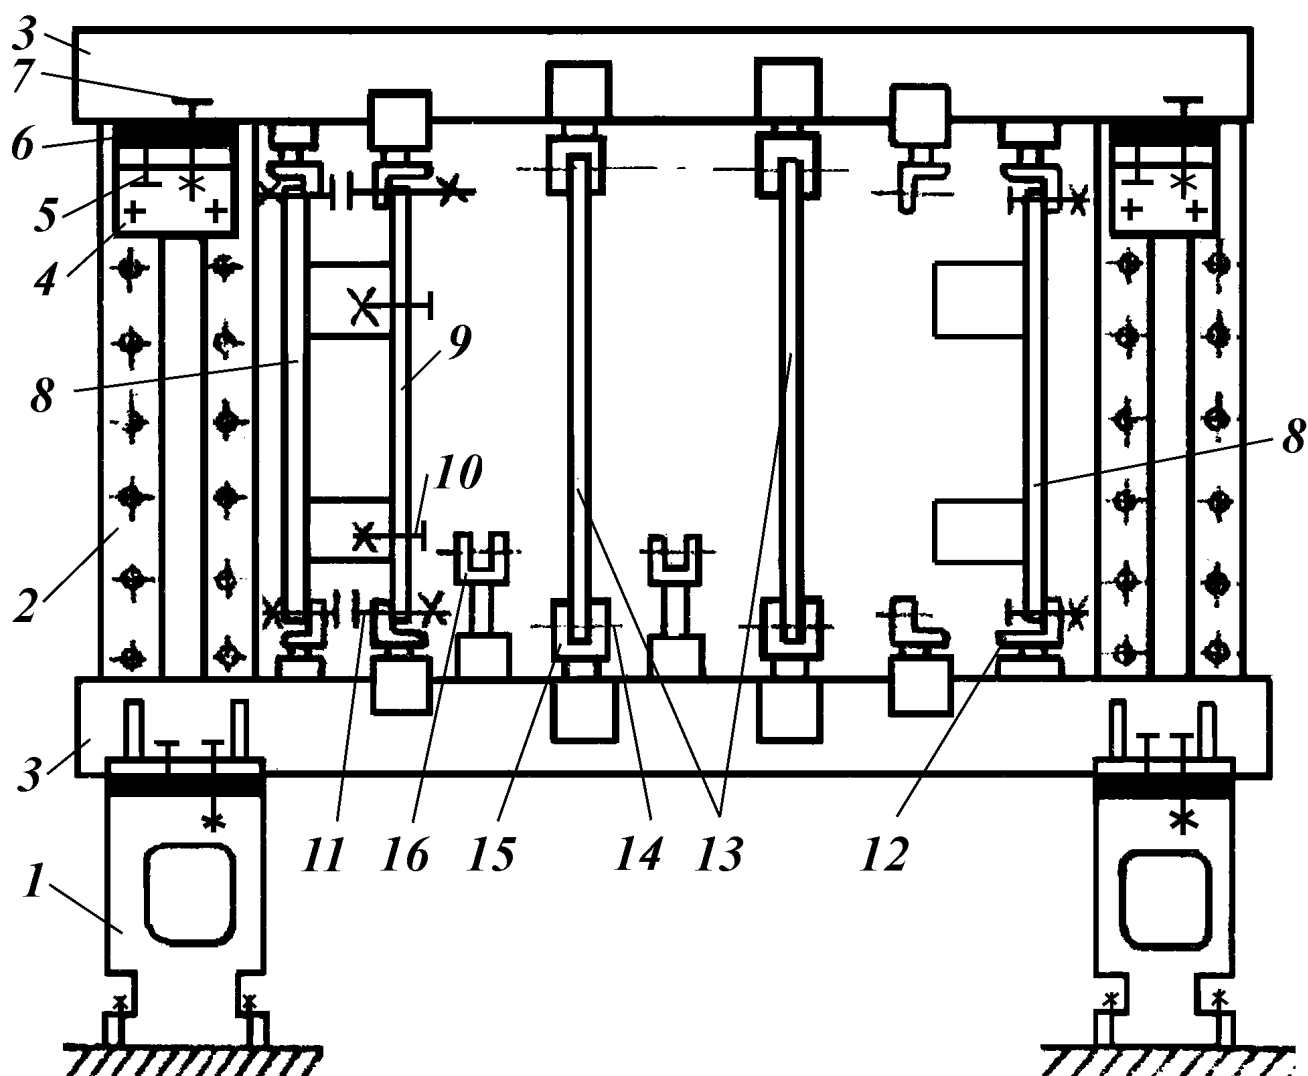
Основные элементы СП (на стадии монтажа): 1 – основание; 2 – колонна (блок); 3 – балка; 4 – кронштейн; 5 – винт регулировочный (домкратный); 6 – наполнитель (прокладка, цемент НИАТ-МЦ); 7 – болт стяжной; 8 – плита монтажная; 9 – плита стапельная; 10 – болт по БО; 11 – болт по МО; 12 – полувилка (ушко); 13 – рубильник; 14 – штырь по МО; 15 – вилка; 16 – фиксатор вилочного стыка
